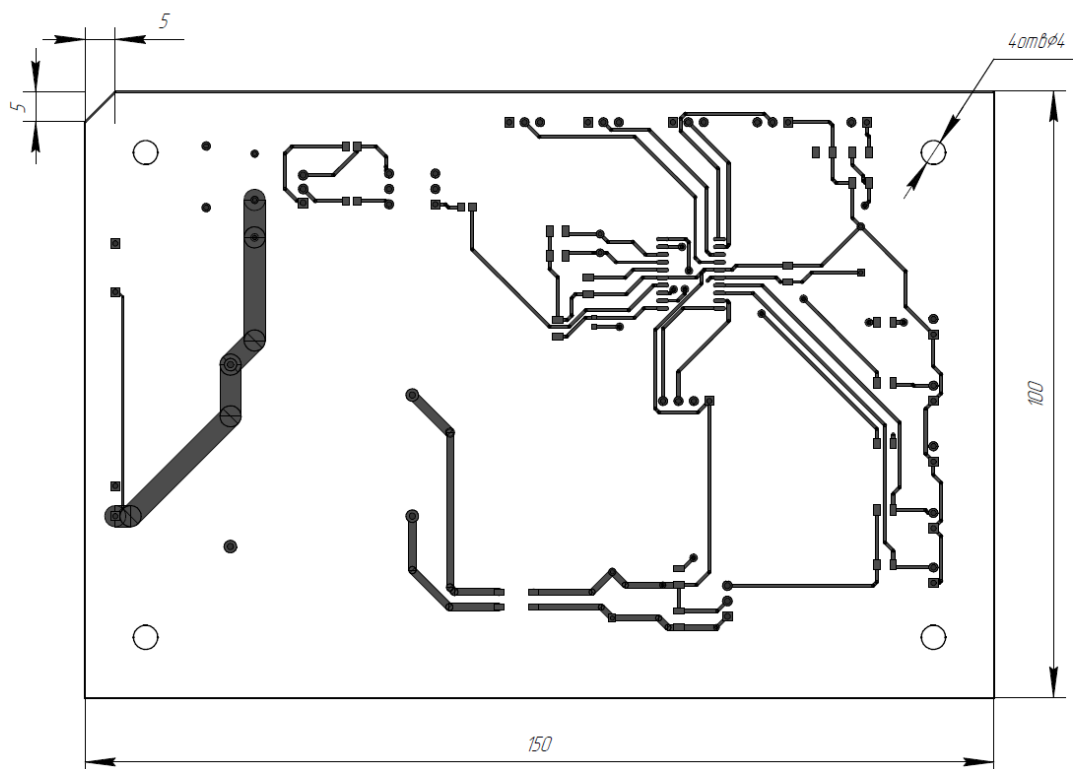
Вид на печатную плату генератора размагничивающего тока
